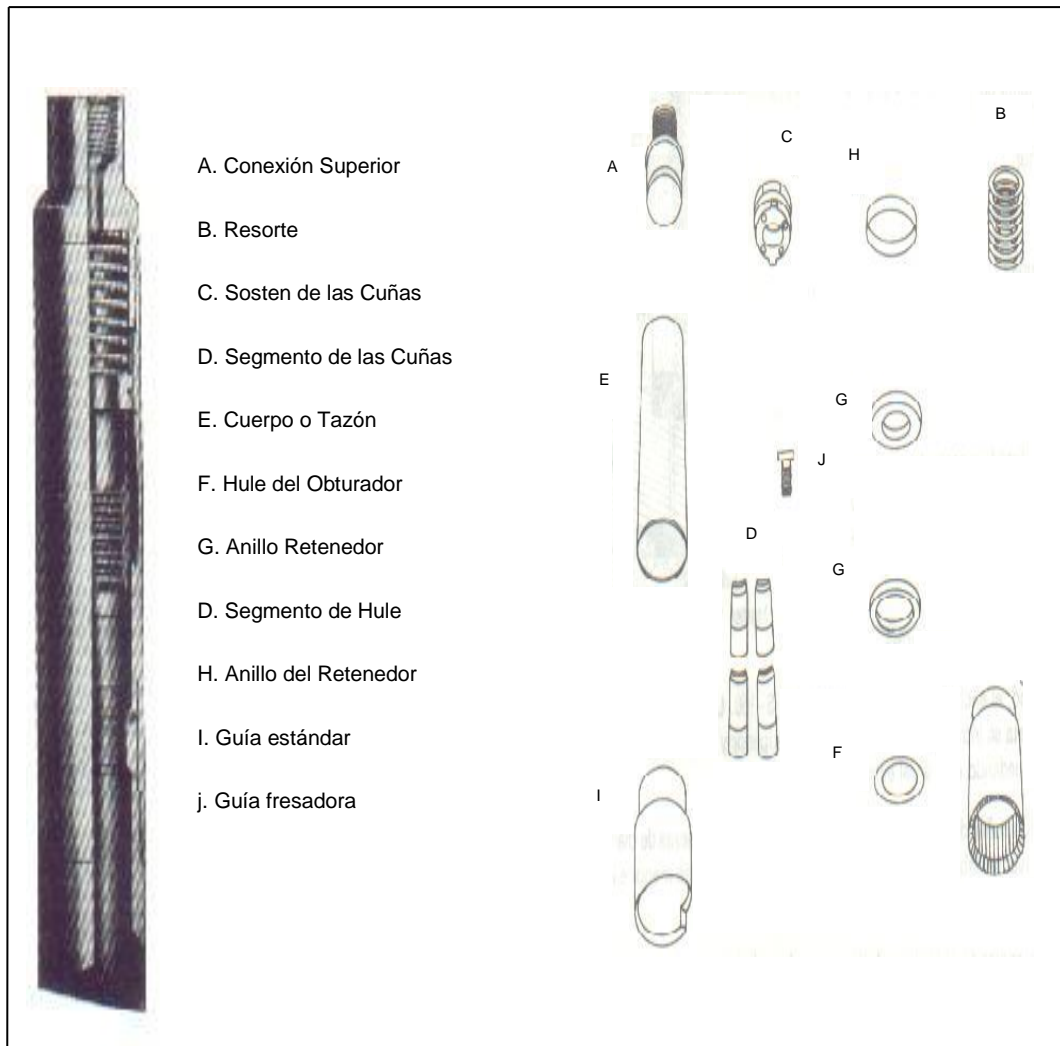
VISTA EXPANSIVA DEL PESCANTE SOLTADOR IZQUIERDO H. E. Y ACCESORIOS
